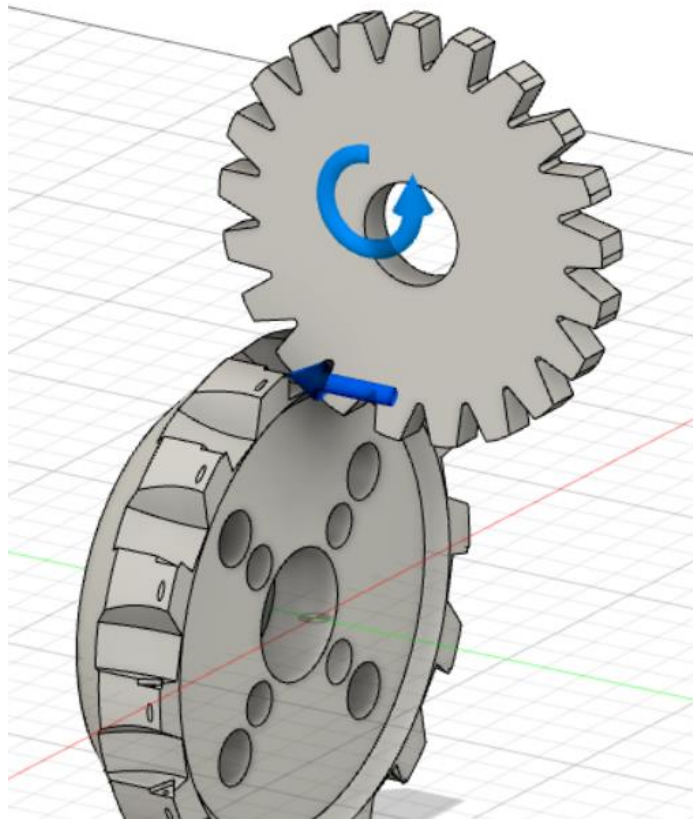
Умовне зображення процесу фрезерування канавок дисковою фрезою та сил і моментів які діють під час обробки
